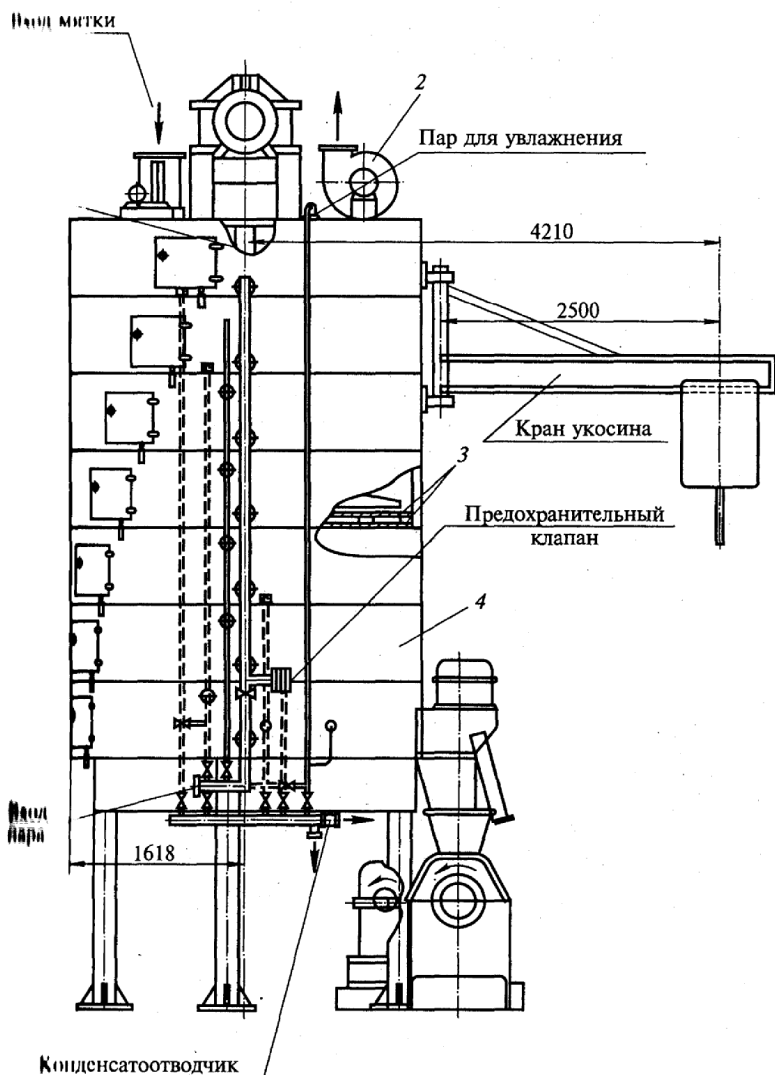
Маслопрессовый агрегат РЗ-МОА:
